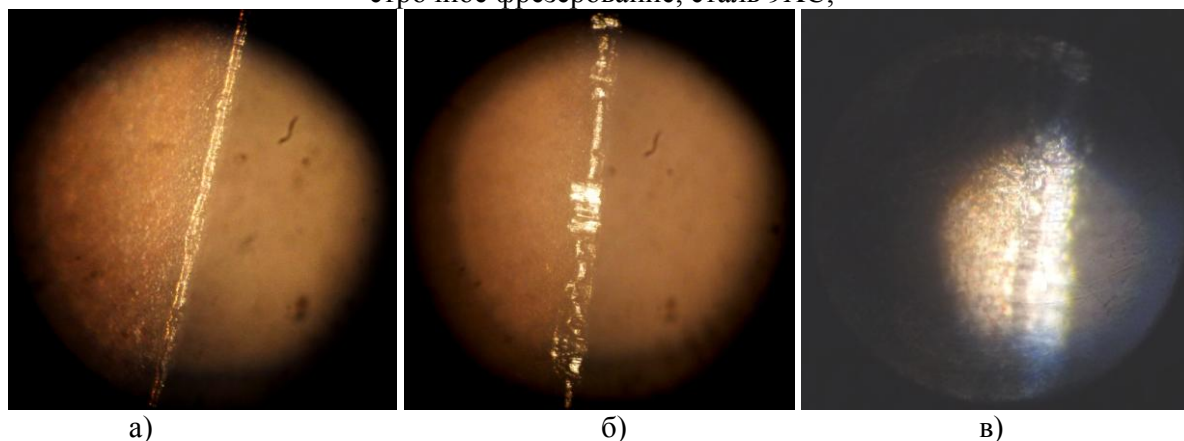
Износ инструмента по задней поверхности: а, б – при фрезеровании с возвратно-качательным движением подачи; в – при построчном фрезеровании
